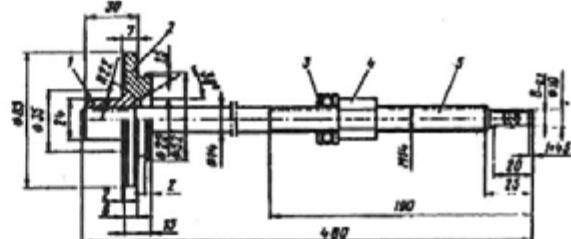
Приспособление для сжатия пружины передней подвески:
